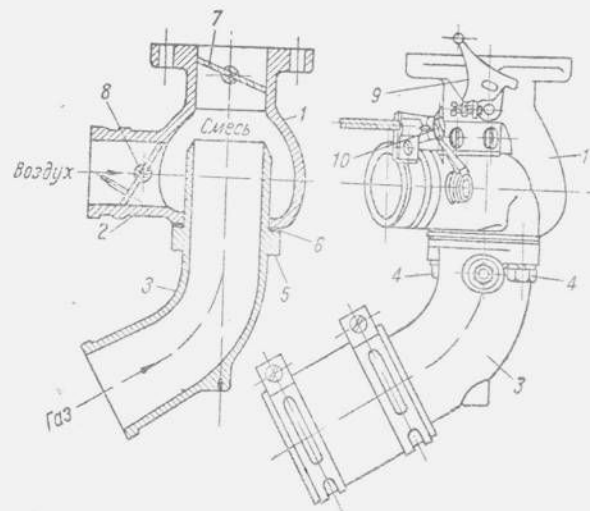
Смеситель газового двигателя ГАЗ-42:
